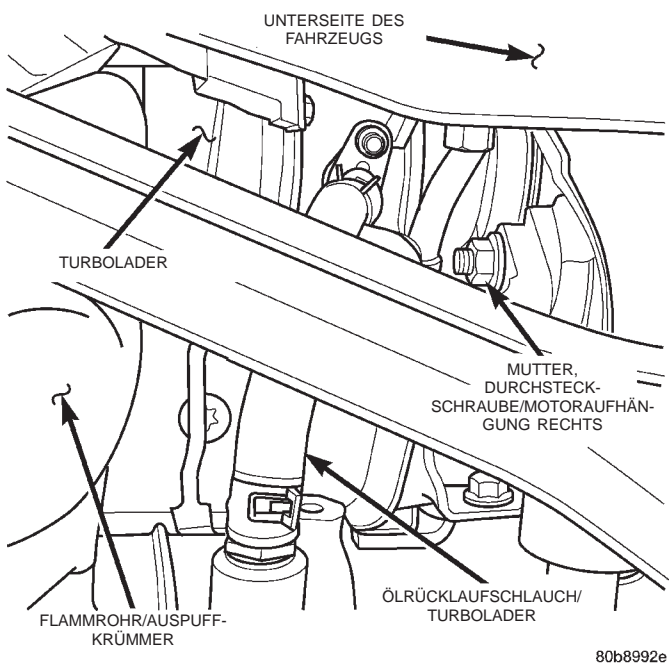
Ölrücklaufschlauch des Turboladers—Lage und Befestigung
